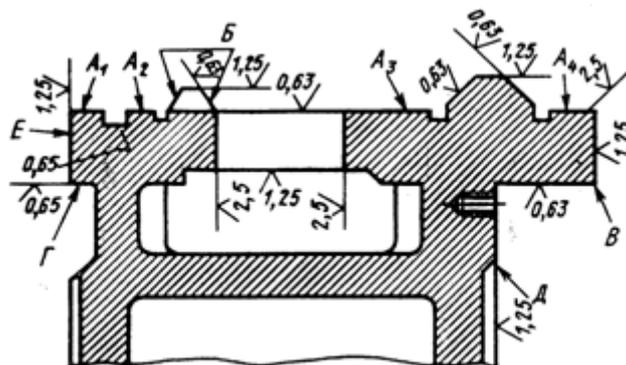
Профиль монолитных направляющих скольжения станины прецизионного токарного станка
